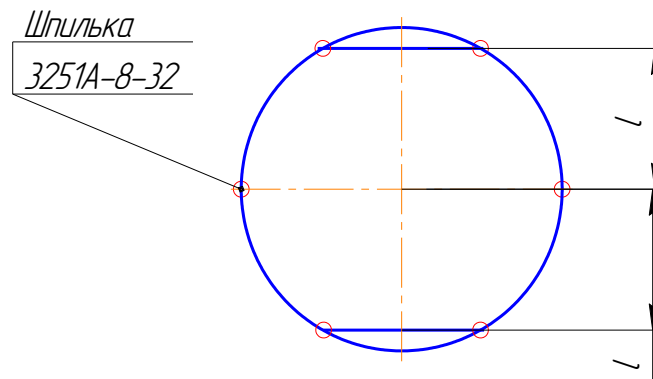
Схема расположения шпилек, крепящих крышку к корпусу.
